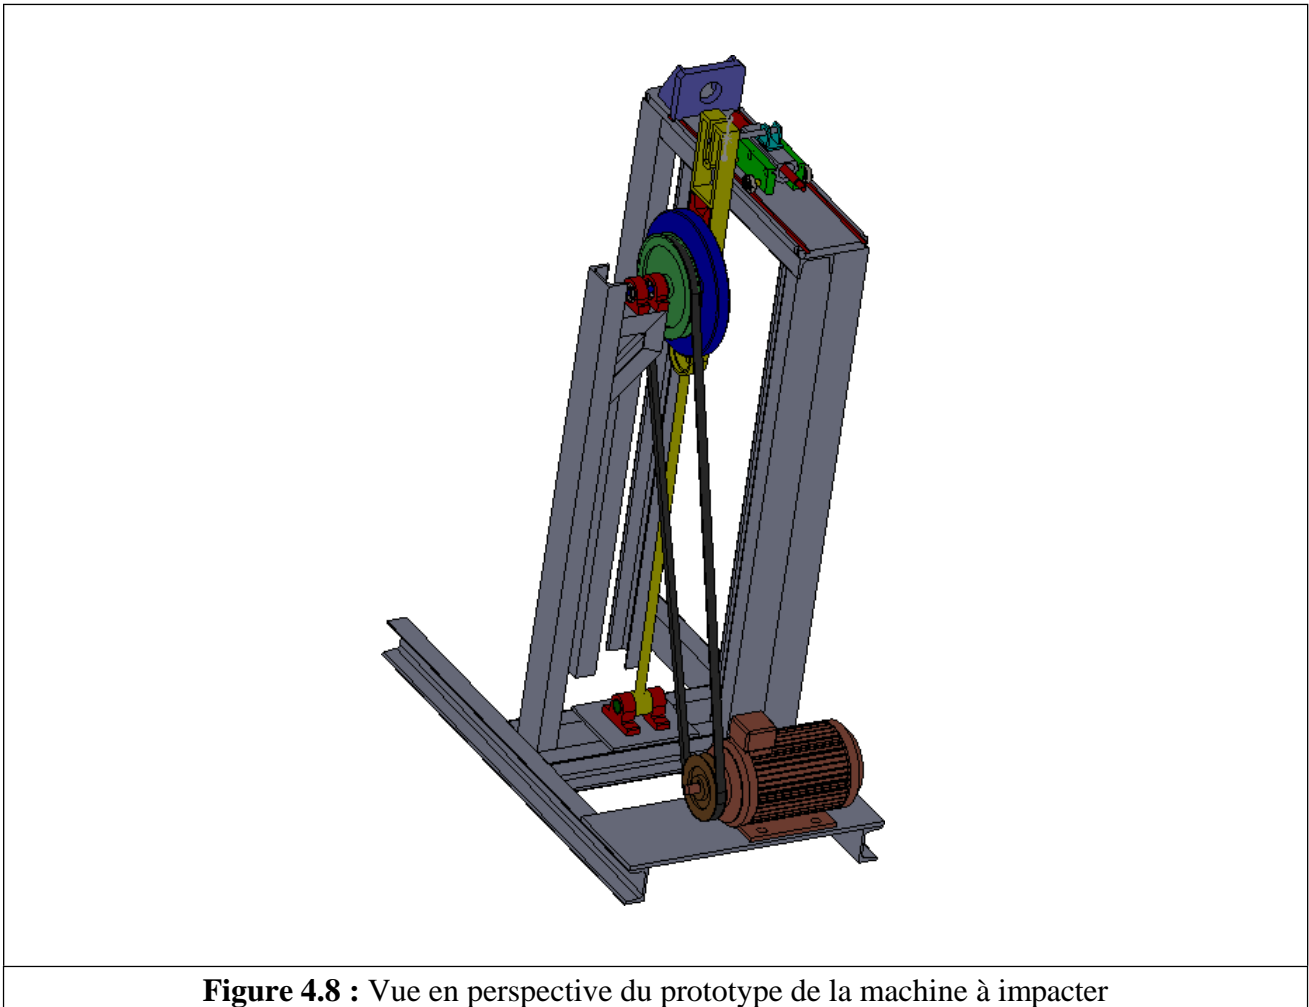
Vue en perspective du prototype de la machine à impacter
